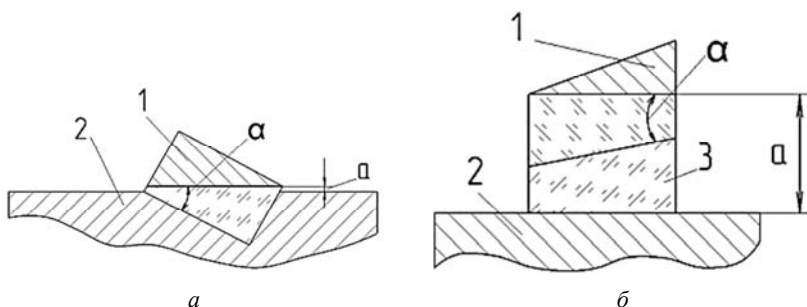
Приспособление металлическое и с сухариками для обработки клиньев:
